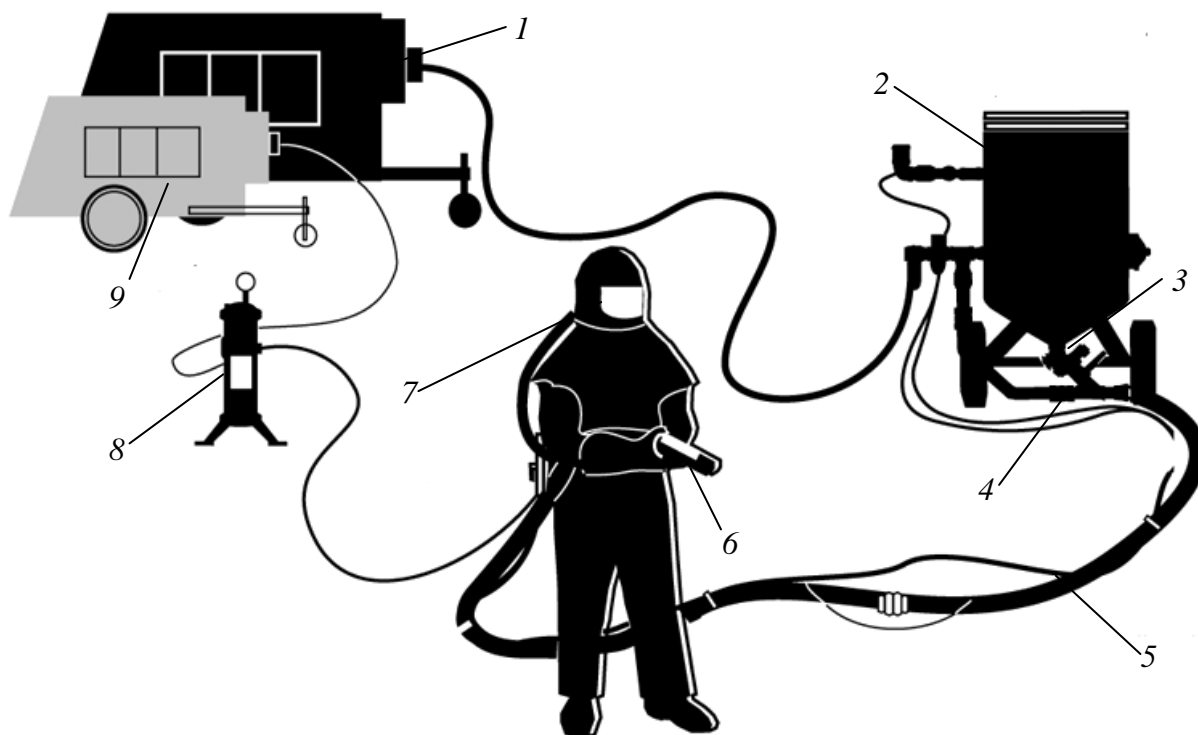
Схема процесса пескоструйной обработки: 1, 9 – компрессор; 2 – пескоструйный аппарат; 3 – кран; 4 – смеситель; 5 – шланг; 6 – рабочая головка; 7 – защитный костюм; 8 – фильтр
